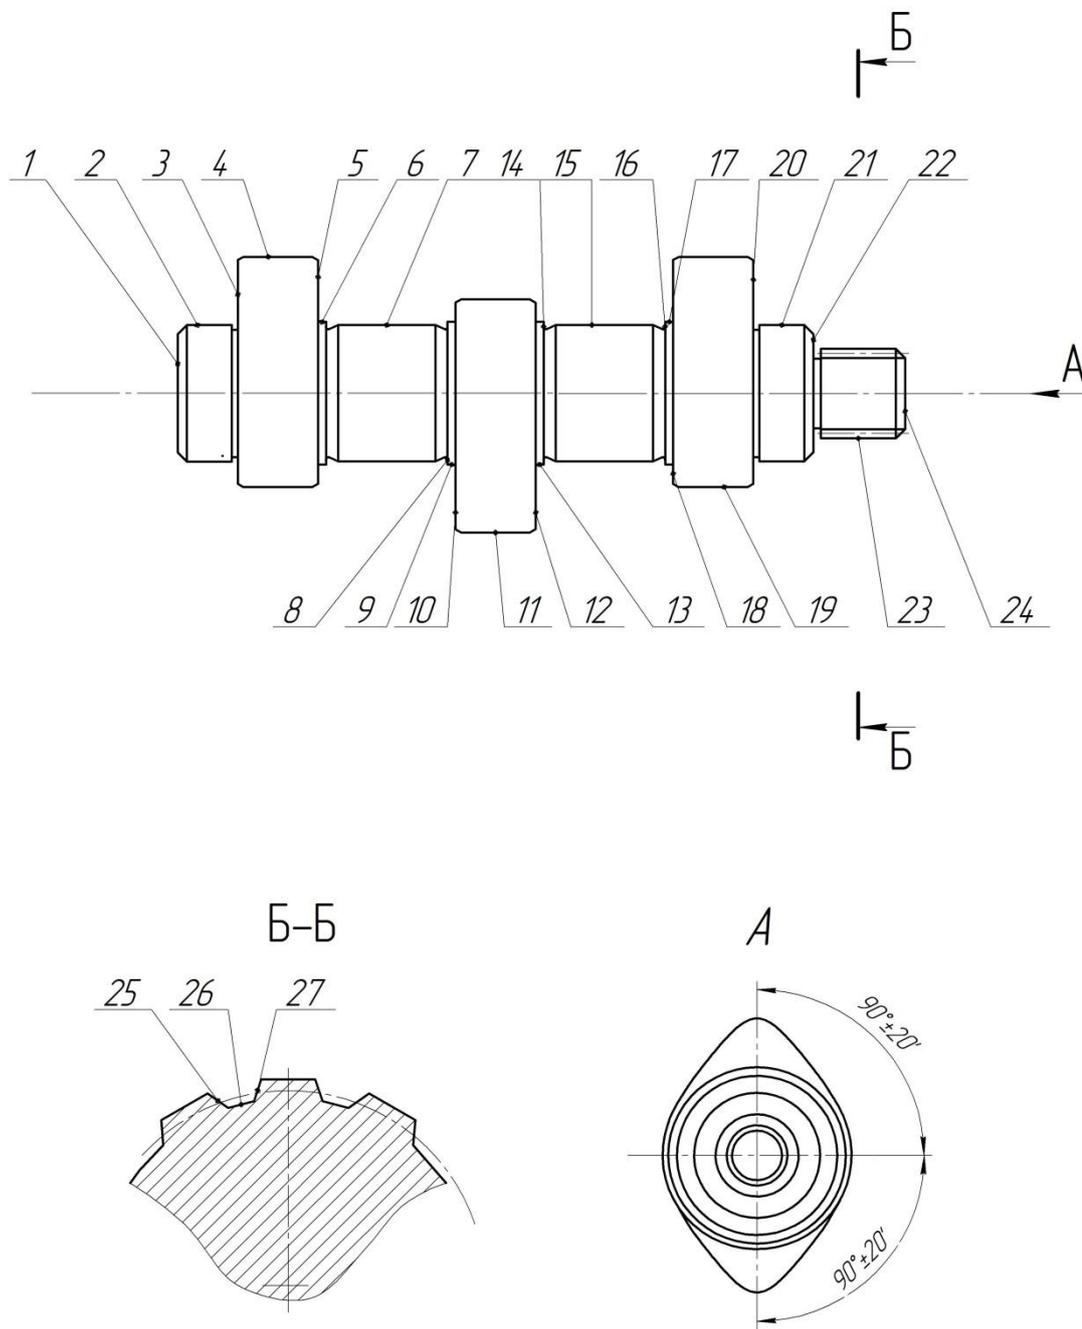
Деталь - «Вал распределительный», общий вид
